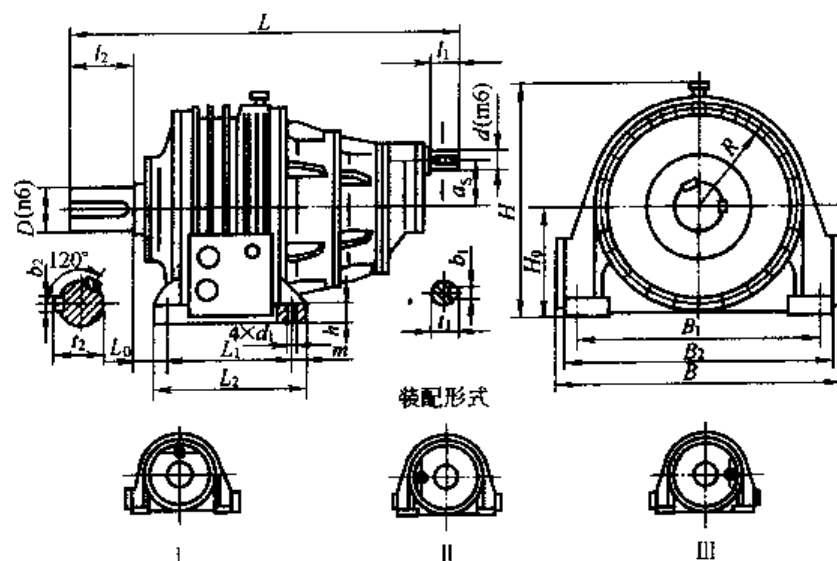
定轴线圆柱齿轮-行星传动装配形式
